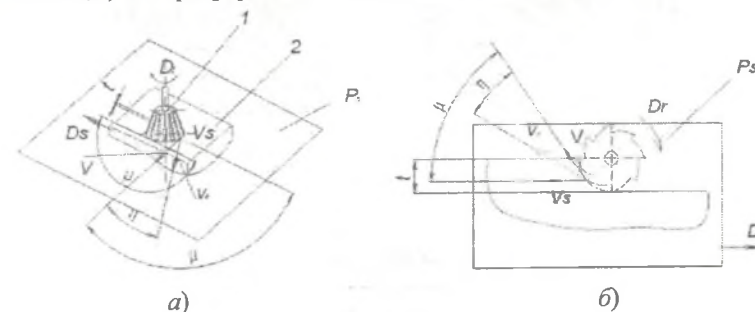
Кинематические схемы торцового (а) и периферийного (б) фрезерования:
